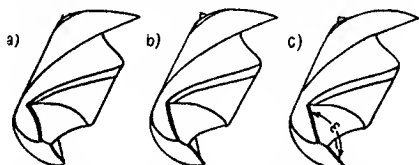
Falscher Bohreranschliff mit rückgewölbter Hauptschneide (a) oder vorgewölbter Hauptschneide (b), richtiger Bohreranschliff mit gerader Hauptschneide und richtigem Spitzenwinkel (c)
